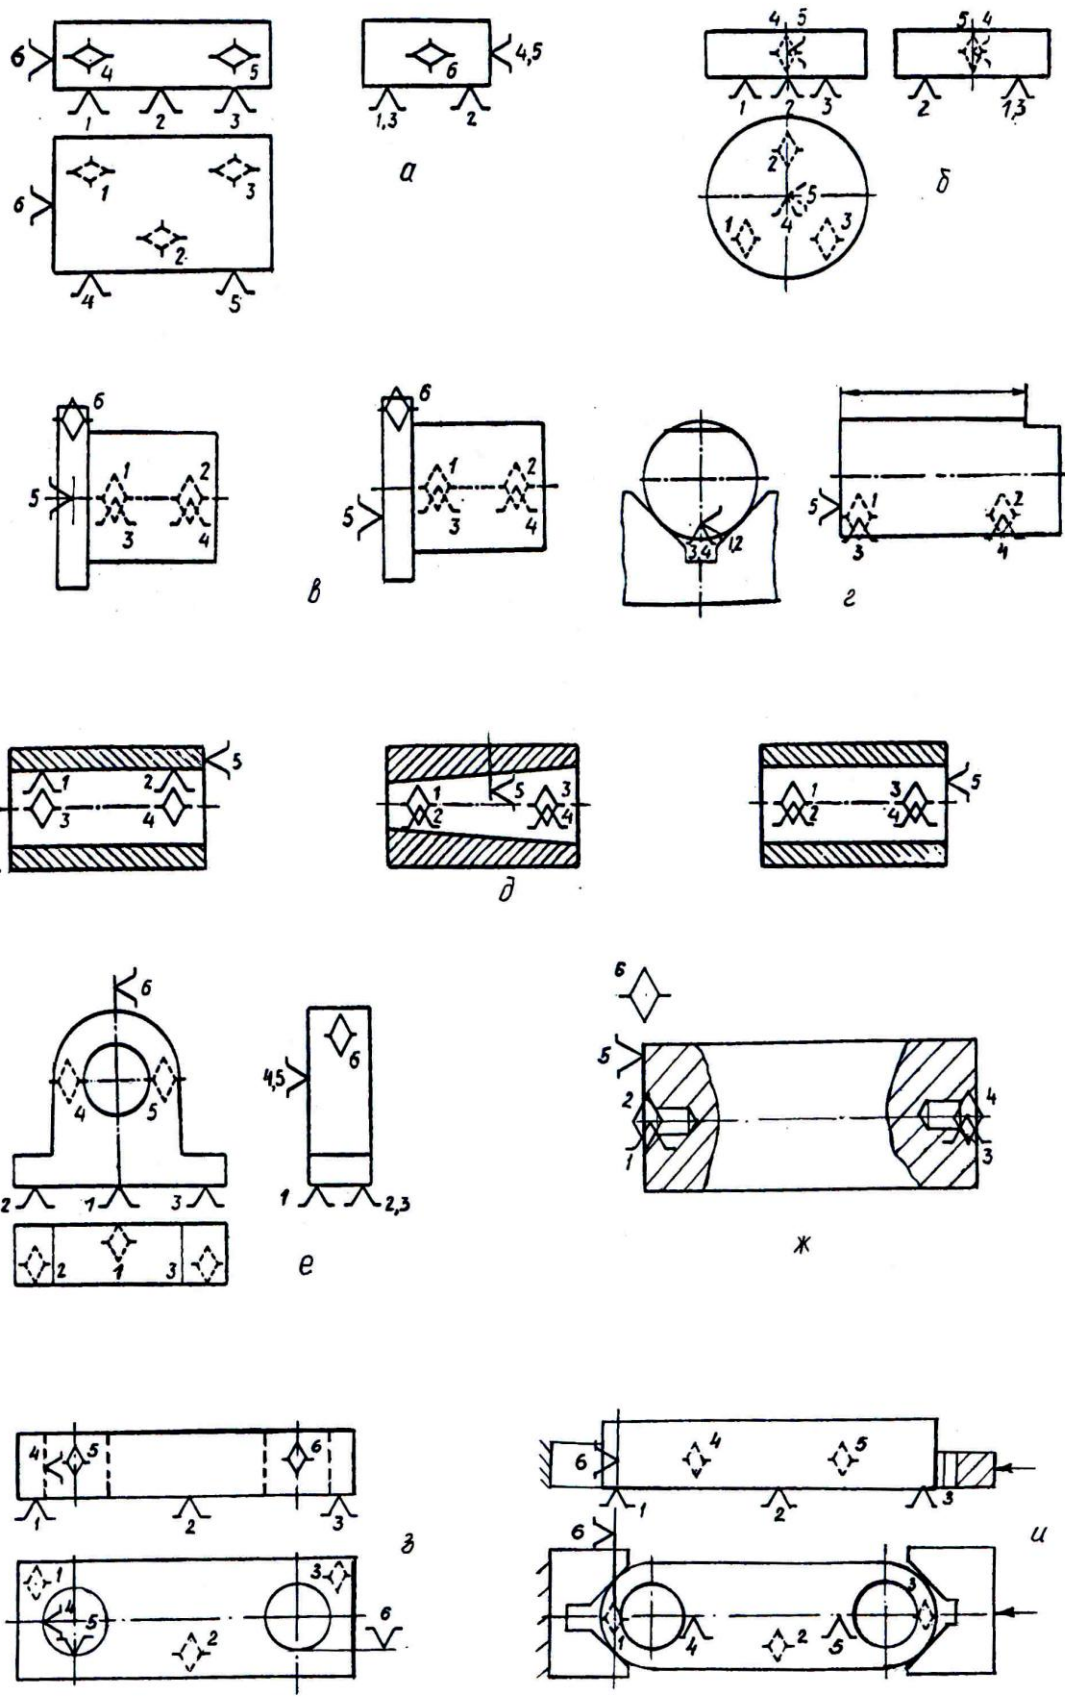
Распространенные схемы базирования заготовок.
